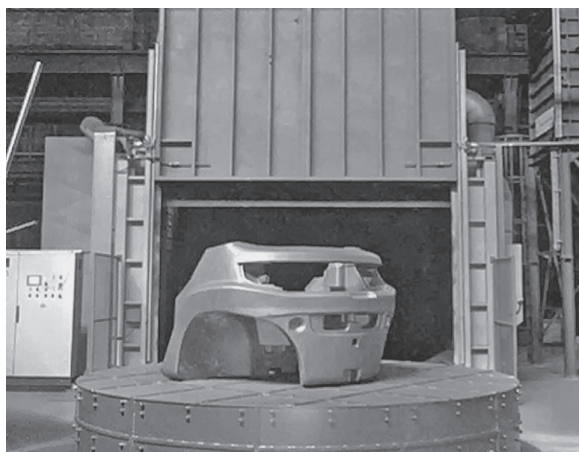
Дробеметная камера очистки отливок с поворотным столом
